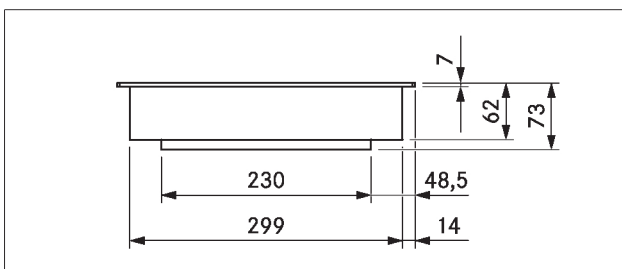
CKT apparatets dimensjoner sett forfra
